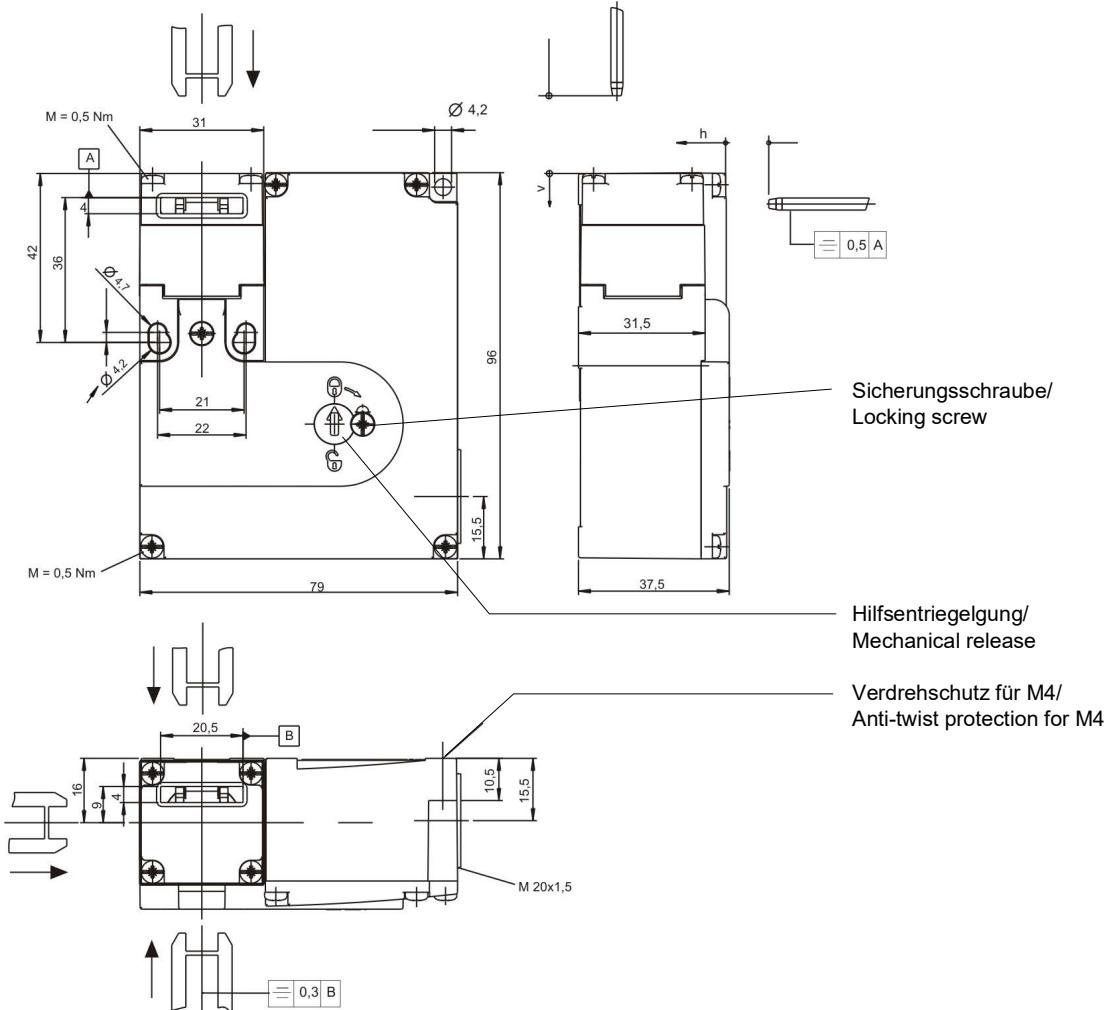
Maßzeichnung ZM / Dimensional drawing ZM
